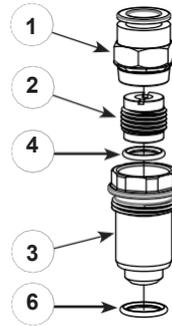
Retrofit Kit de tube et de bouchon de fluide
